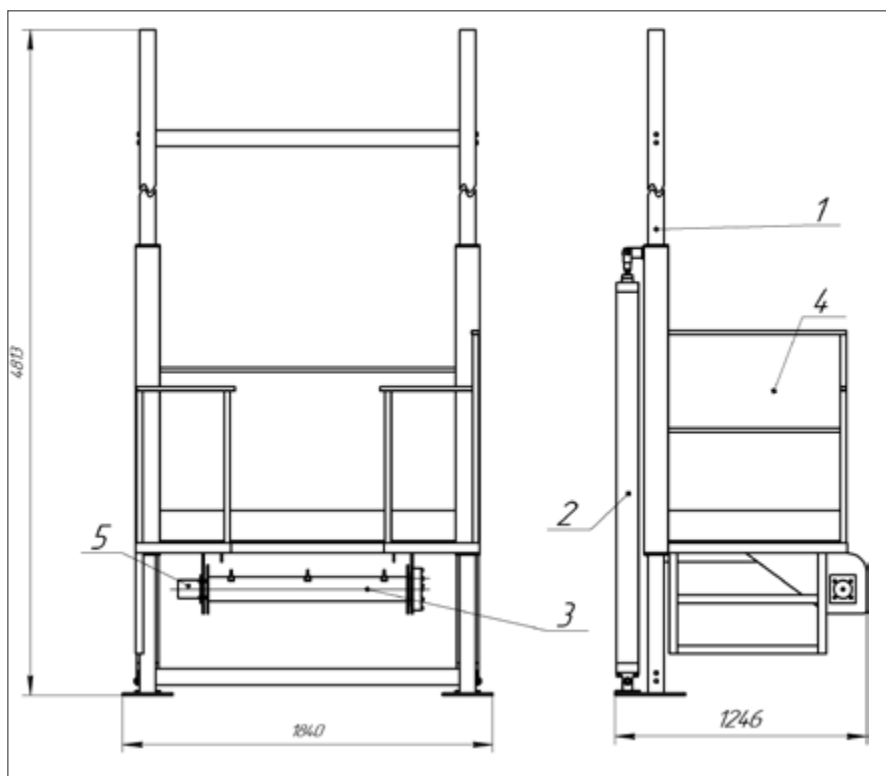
Общий вид пневматической шкуроемной машины: 1 – подъемно-опускная площадка; 2 – пневмоцилиндры; 3 – барабан; 4 – каркас; 5 – мотор-редуктор
